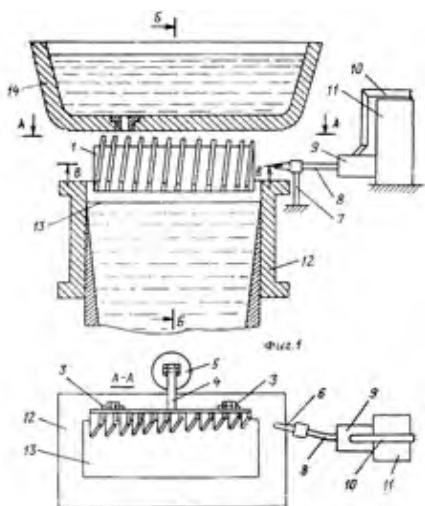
Устройство для подачи порошкообразных шлаковых смесей в кристаллизатор при многоручьевой разливке [5]
